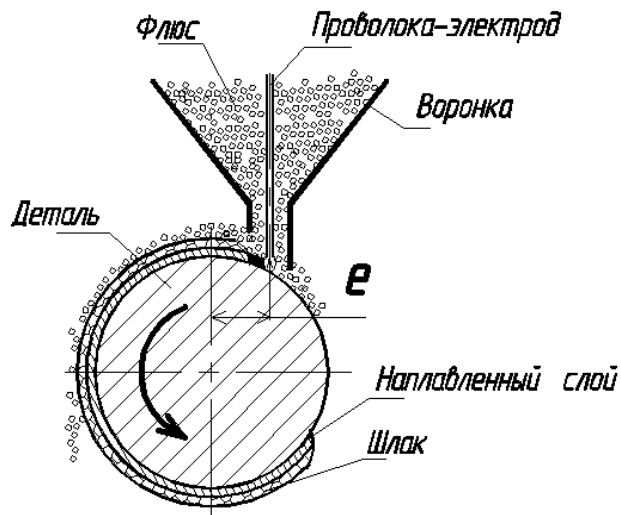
Принцип наплавки под слоем флюса. [17]
